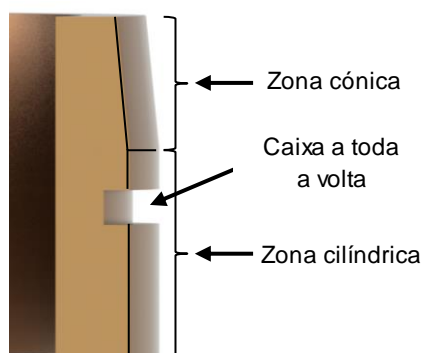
Perfil da cinta de travamento visto em corte.
